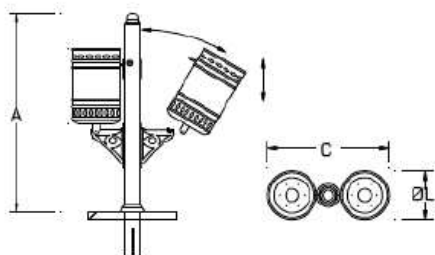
Croquis de Papeleras Tenerife Doble. (Fuente: <http://www.bricantel.pt/es/>)
